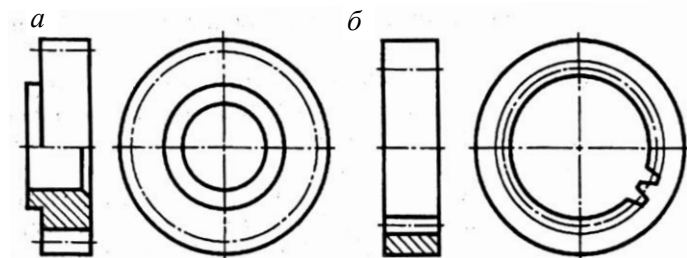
Условное изображение цилиндрических зубчатых колес с наружным (а) и внутренним (б) зубчатым венцом
